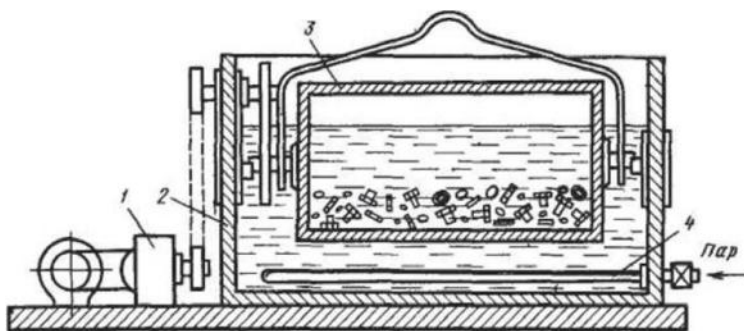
Очистка деталей в галтовочных барабанах:
